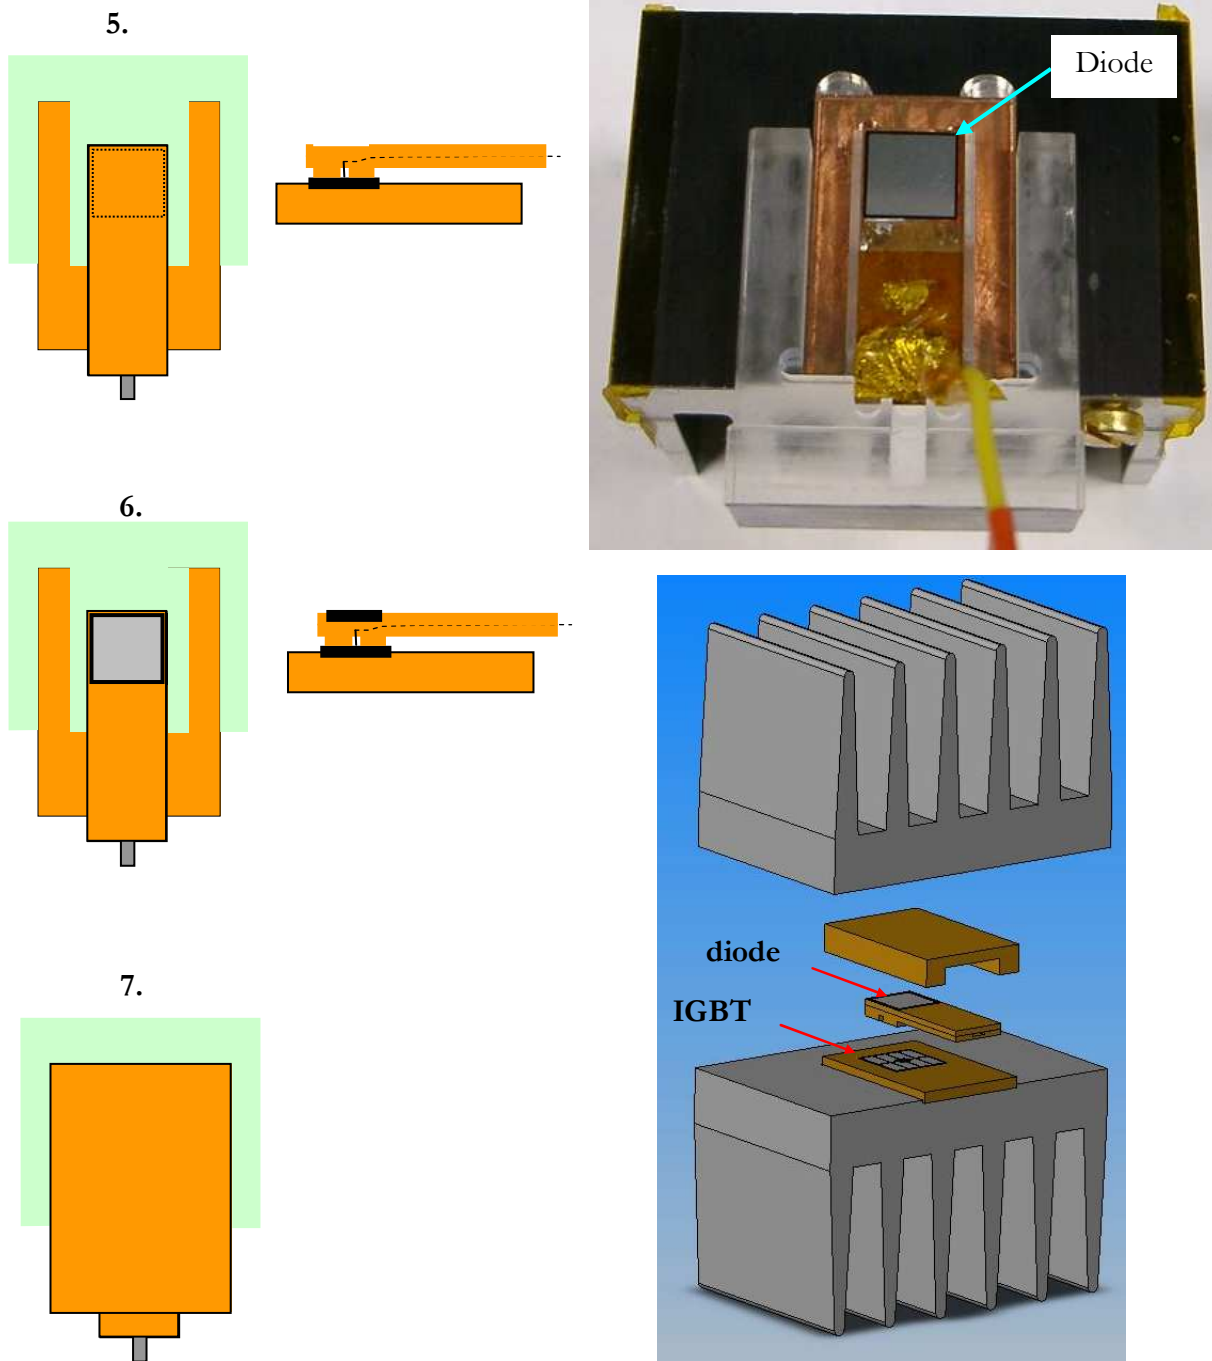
Etapes 5 à 7 de l'assemblage et vue 3D du hacheur CoC première version
